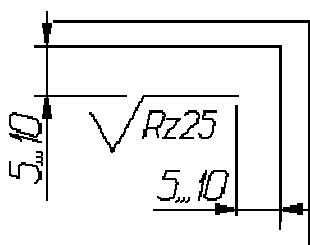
Указание шероховатости одинаковой для всех поверхностей изделия
